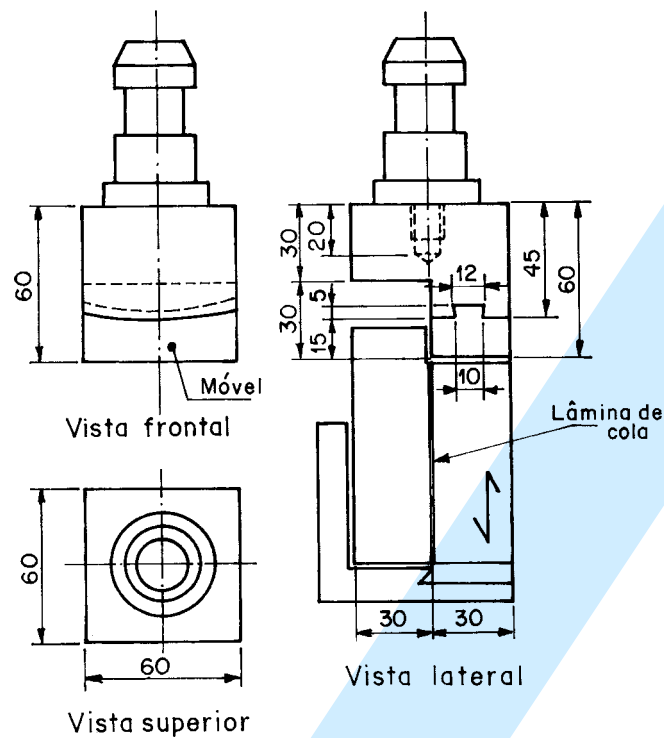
Arranjo de ensaio para cisalhamento na lâmina de cola, na direção paralela às fibras
